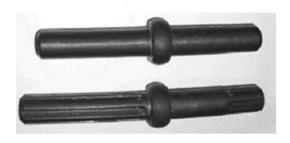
CG125 摩托车主轴花键冷挤压成形件和坯料 Fig. 4 Cold extruded part and blank of CG125 motorcycle's mainshaft
